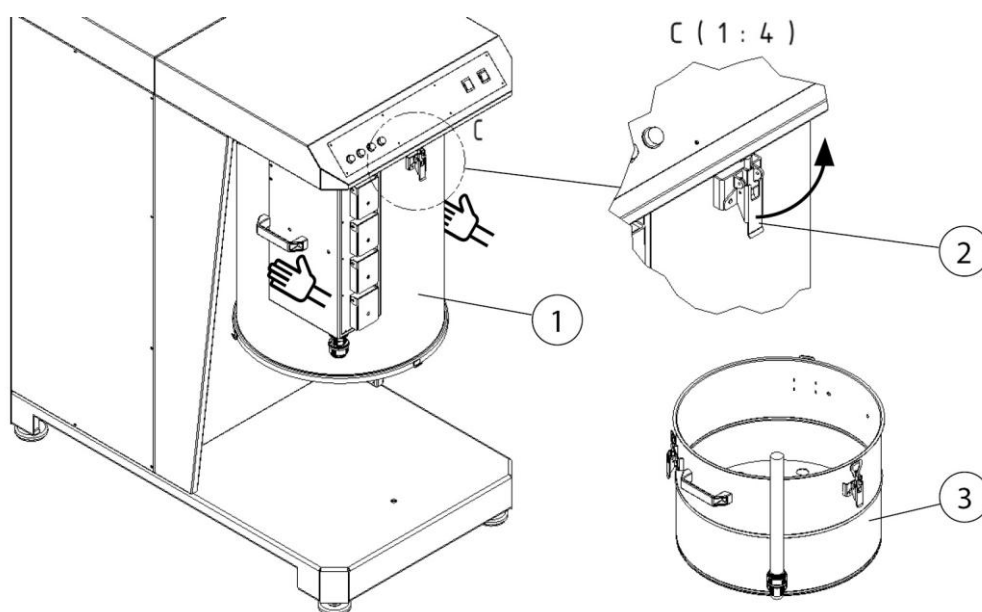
Cambio del filtro – Smontaggio del corpo del filtro
